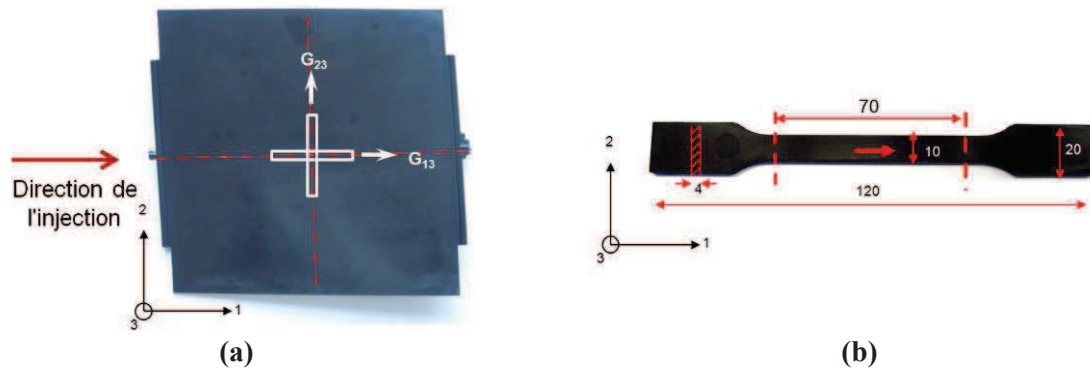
Zones découpées de plaque injectée (a) et d'éprouvette haltère (b) pour les éprouvettes ARCAN-MINES
